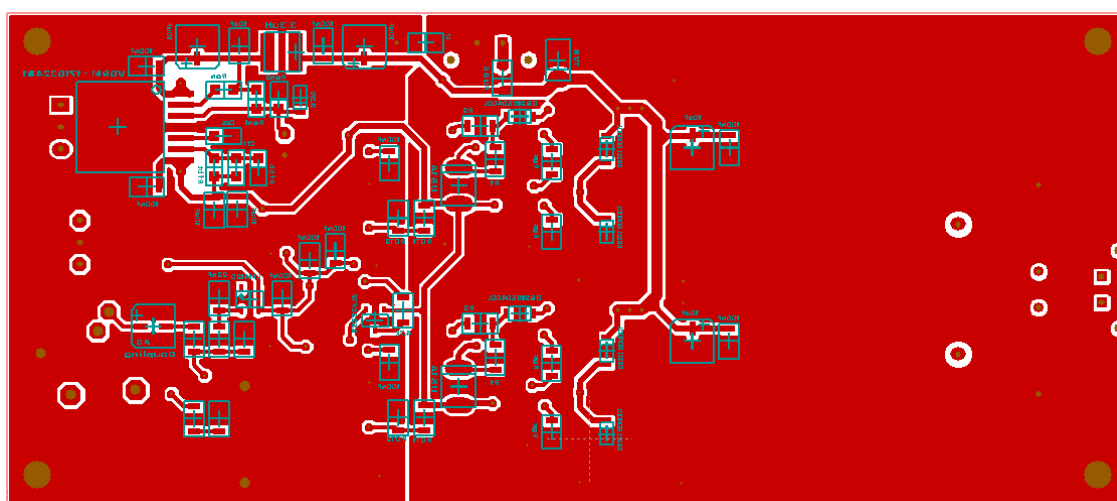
Layout de la cara inferior de la PCB (Fuente: propia)
